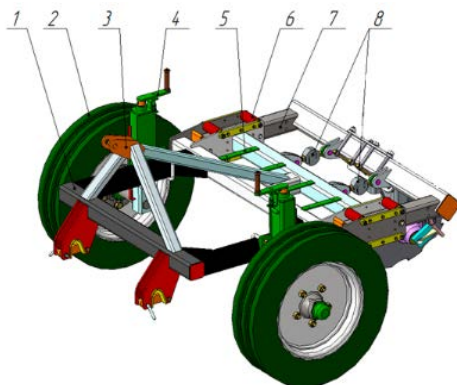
Экспериментальная установка для определения тягового сопротивления предплужников: 1 – рама; 2 – ход колесный; 3 – устройство навесное; 4 – механизм регулировочный; 5 – площадка для грузов; 6 – опора; 7 – рамка подвижная; 8 – тензометрические датчики
